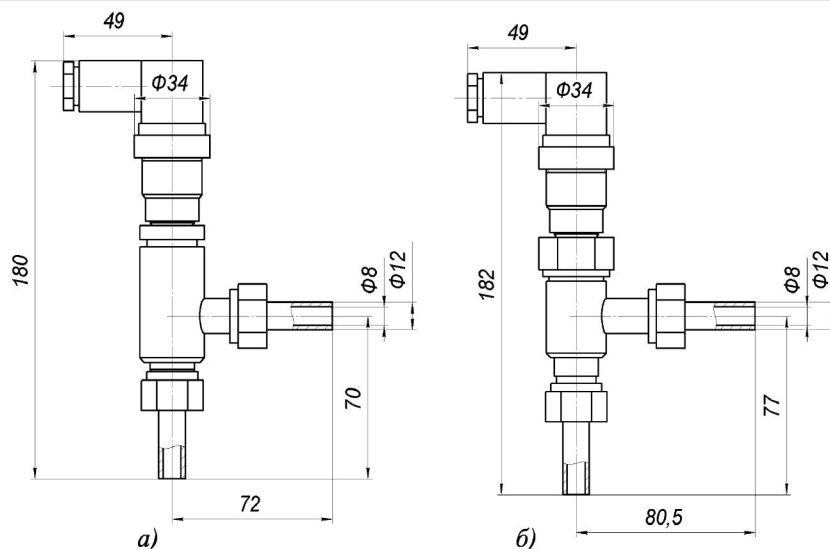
Габаритные и монтажные размеры проточного пассивного датчика ECS-1.15 (0..1000мСм/см) (а); ECS1.16 (0..1000мкСм/см) (б)
